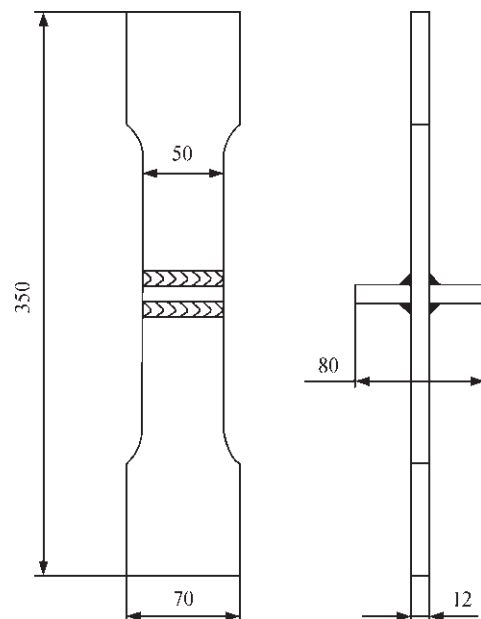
Форма и геометрические размеры образцов таврового сварного соединения
